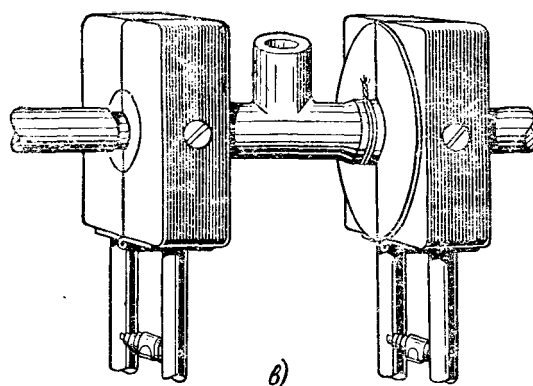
Специальные принадлежности для газовой сварки.
